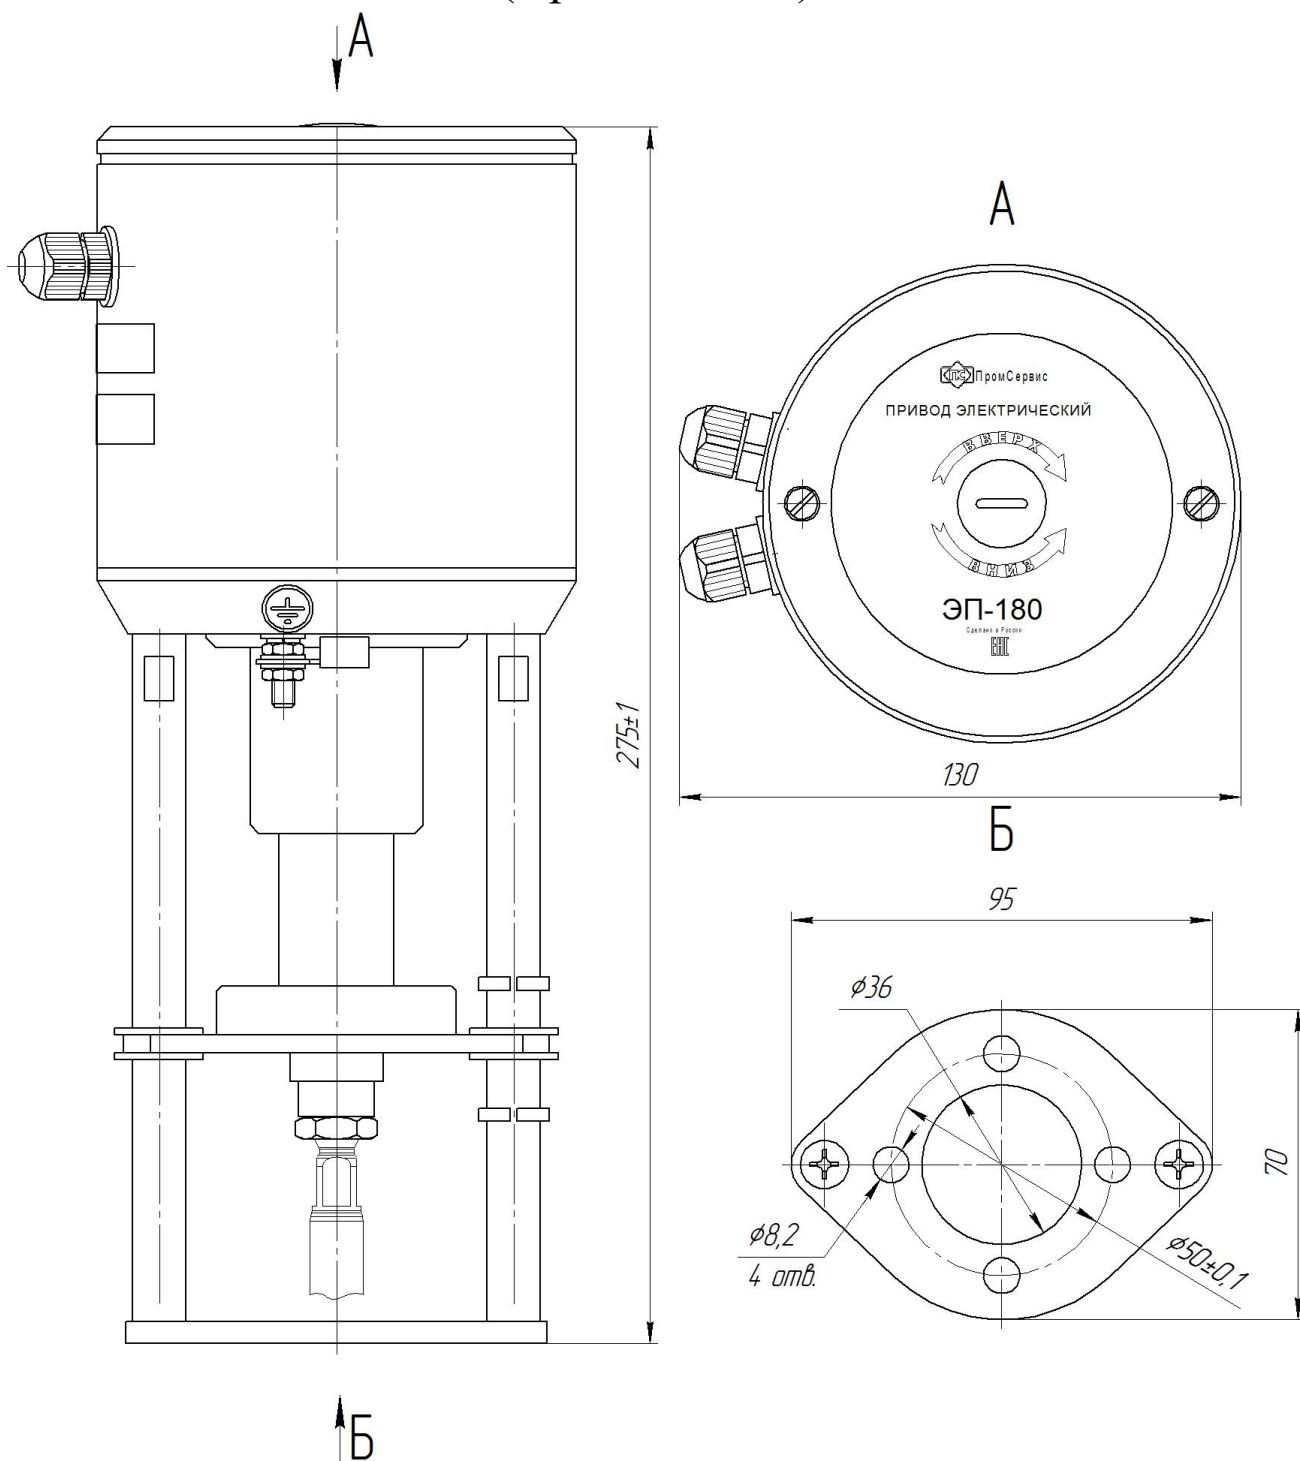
габаритные и присоединительные размеры привода исполнения ЭП-180-02/2
